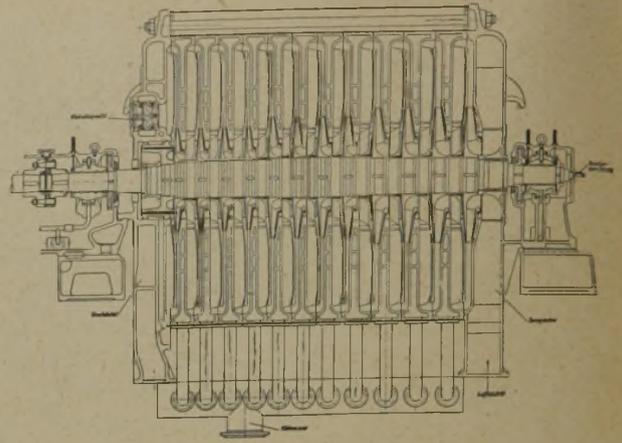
Längsschnitt durch einen innengekühlten Kompressor
